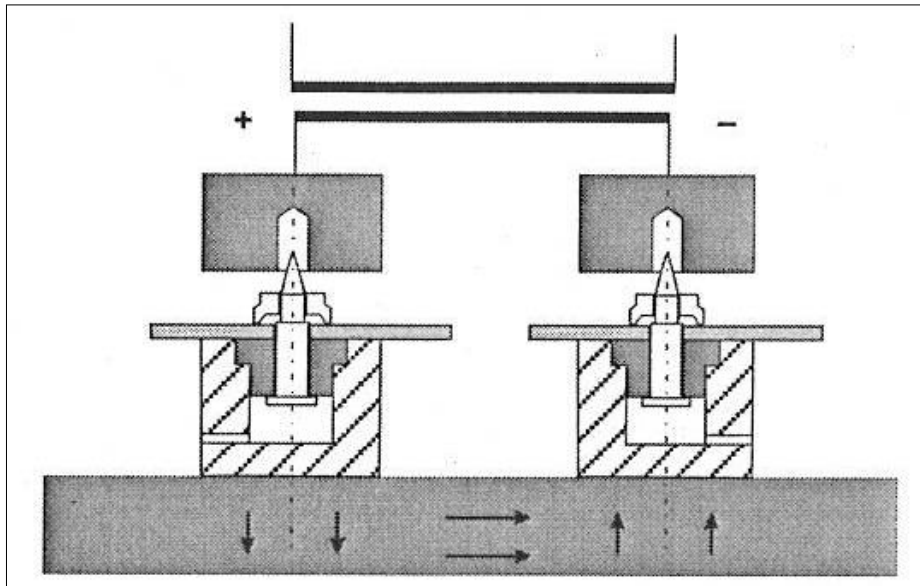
Soldadura simultánea de tuercas por proyección.
